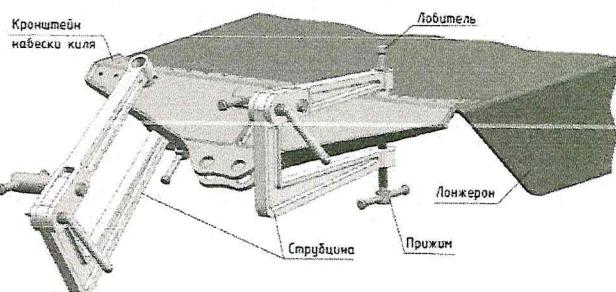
Общий вид кондукторной скобы-клещей, установленной на конструкции
